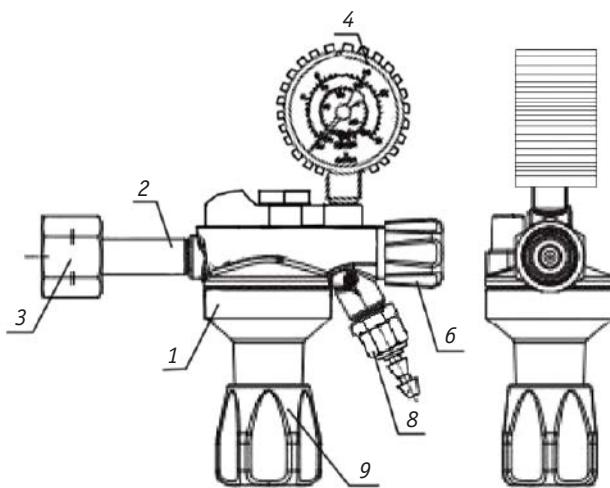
Схема редуктора баллонного газового TECH CONTROL PB (пропан).
